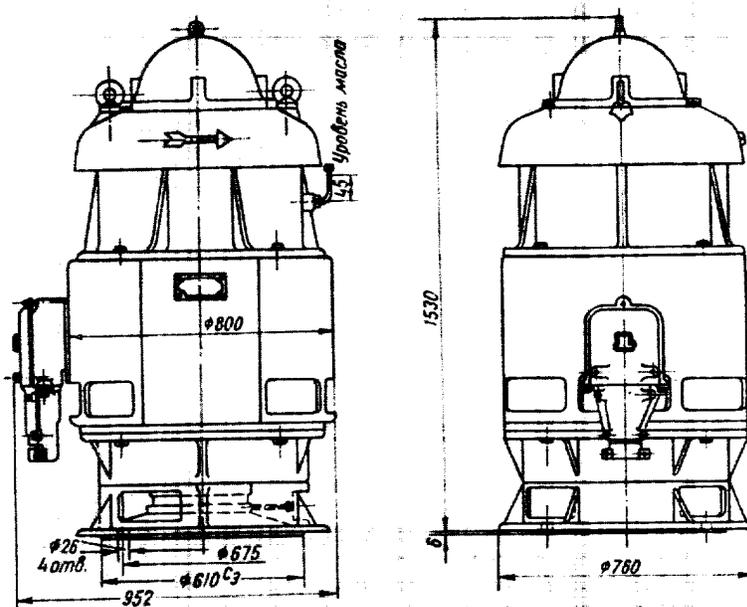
Размеры электродвигателя ДАМВШ 114-4 и ДАМВШ 115-4
